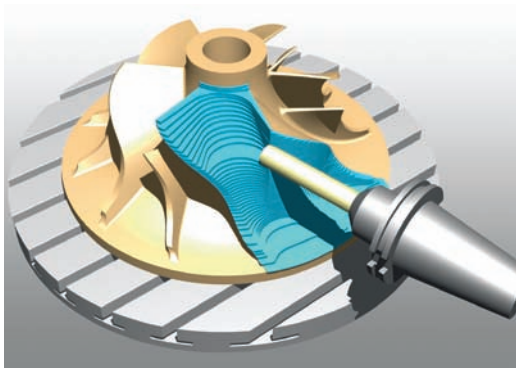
Restmaterialbearbeitung an einem Impeller mit angestelltem Werkzeug. (Bild: Schott Systeme)
